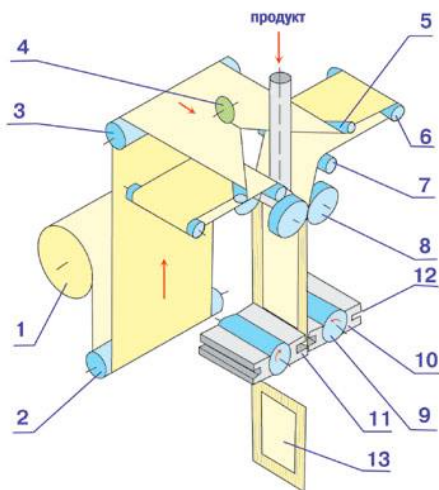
Компонування машини з роторними губками зварювання: 1 – рулон плівки; 2, 3, 5, 6, 7 – натяжні ролики; 4 – розрізний ніж; 8 – ролики поздовжнього зварювання; 9 – ротор; 10, 12 – губки поперечного зварювання; 11 – відрізний механізм; 13 – готовий пакет
